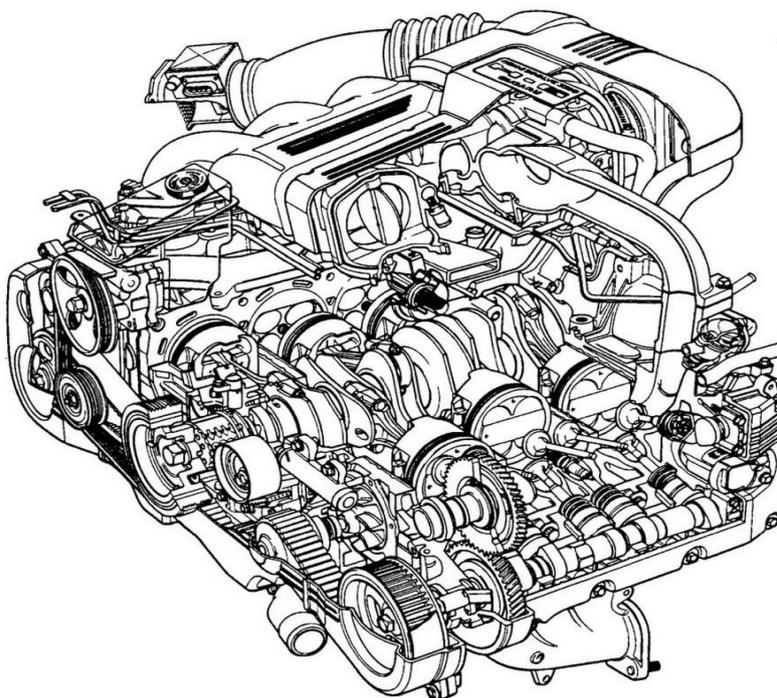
Схема конструкции оппозитного двигателя внутреннего сгорания.
